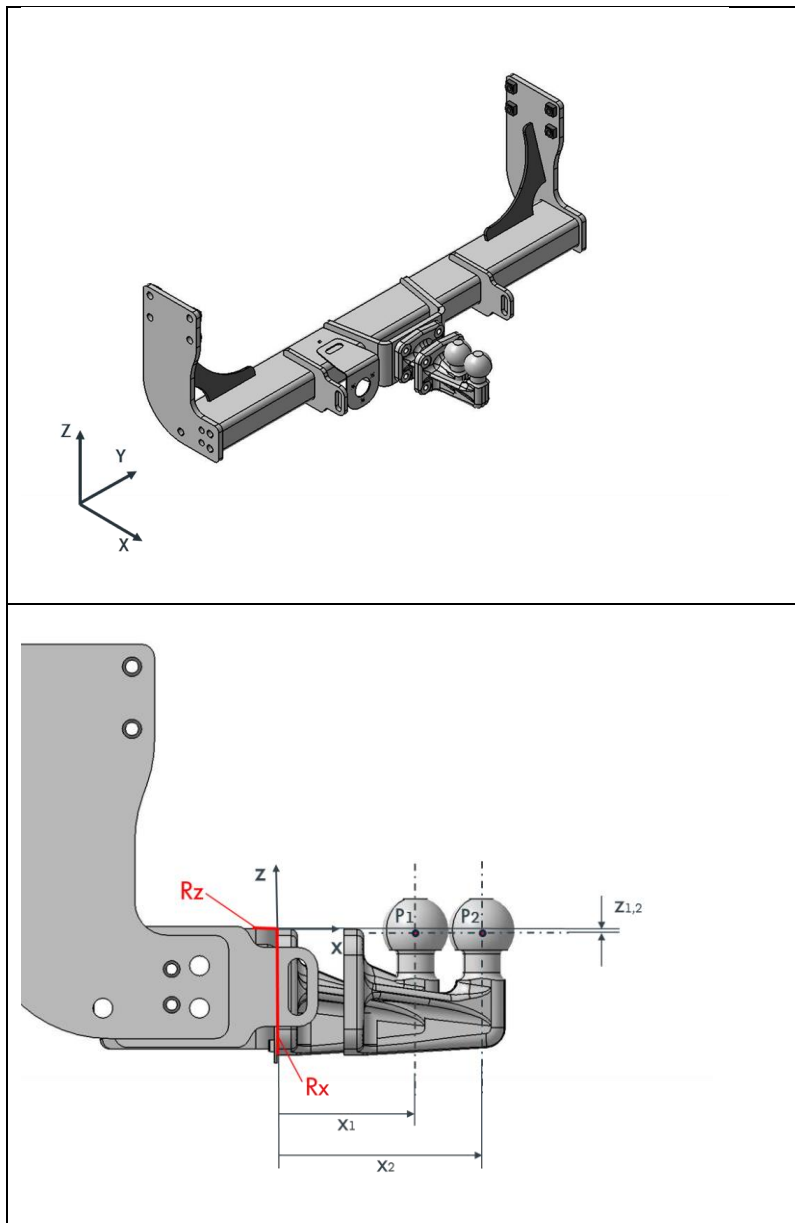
Posición de cabezal esférico: enganche para remolque rígido (P1) y enganche para remolque desmontable (P2)
